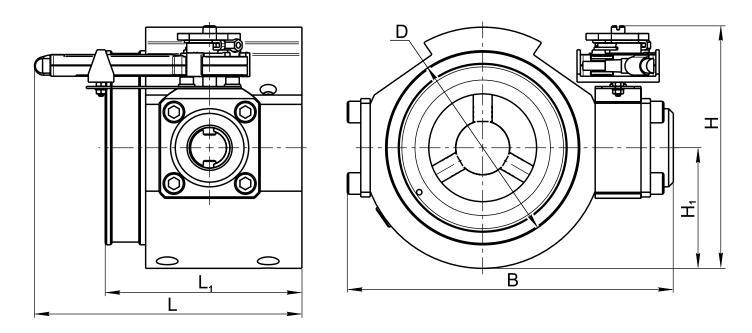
Габаритные и присоединительные размеры для смесителей типа СГ...-М
